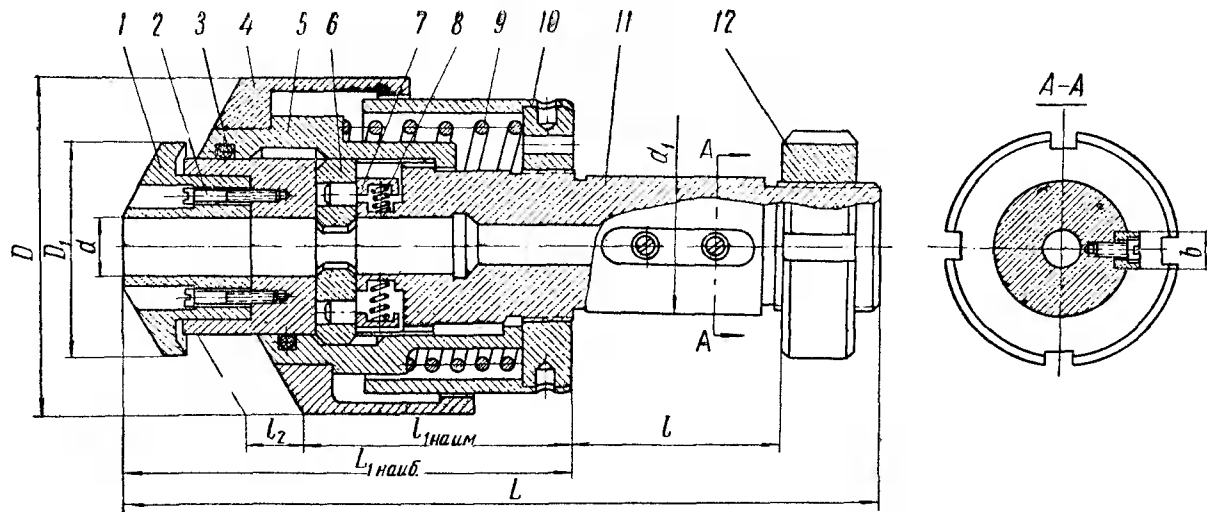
Автоматический патрон к вертикально-протяжным станкам:
